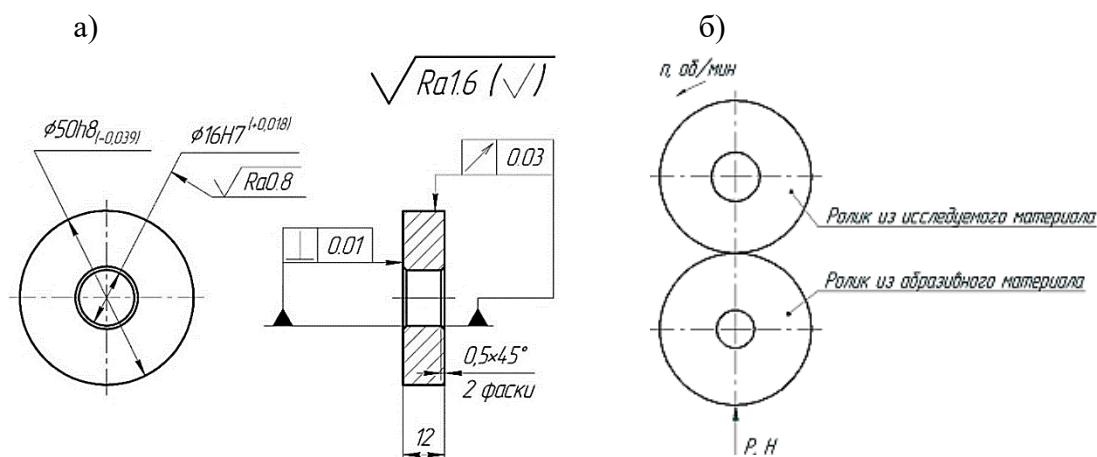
Схема образцов для проведения трибологических испытаний: а) ролик верхний (подвижный); б) нижний абразивный ролик (неподвижный).
